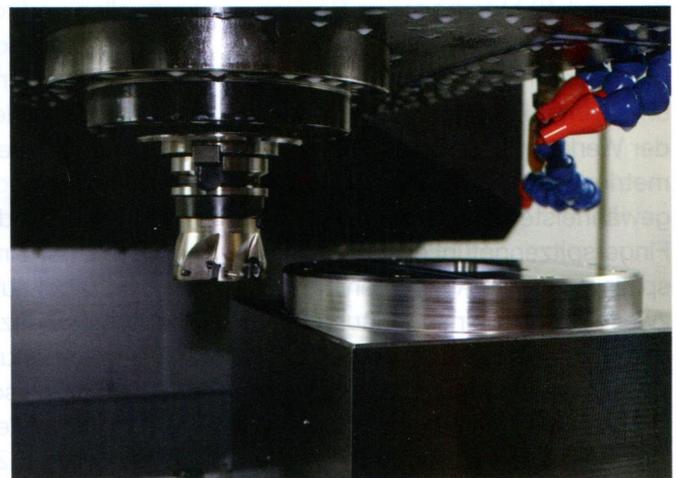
Bei dieser Adapterplatte für Bohrgestänge wird die Passung 220 h6 am Bolzen mit einer Toleranz von 0/-0,029 mm in nur zwei Arbeitsschritten erzeugt
